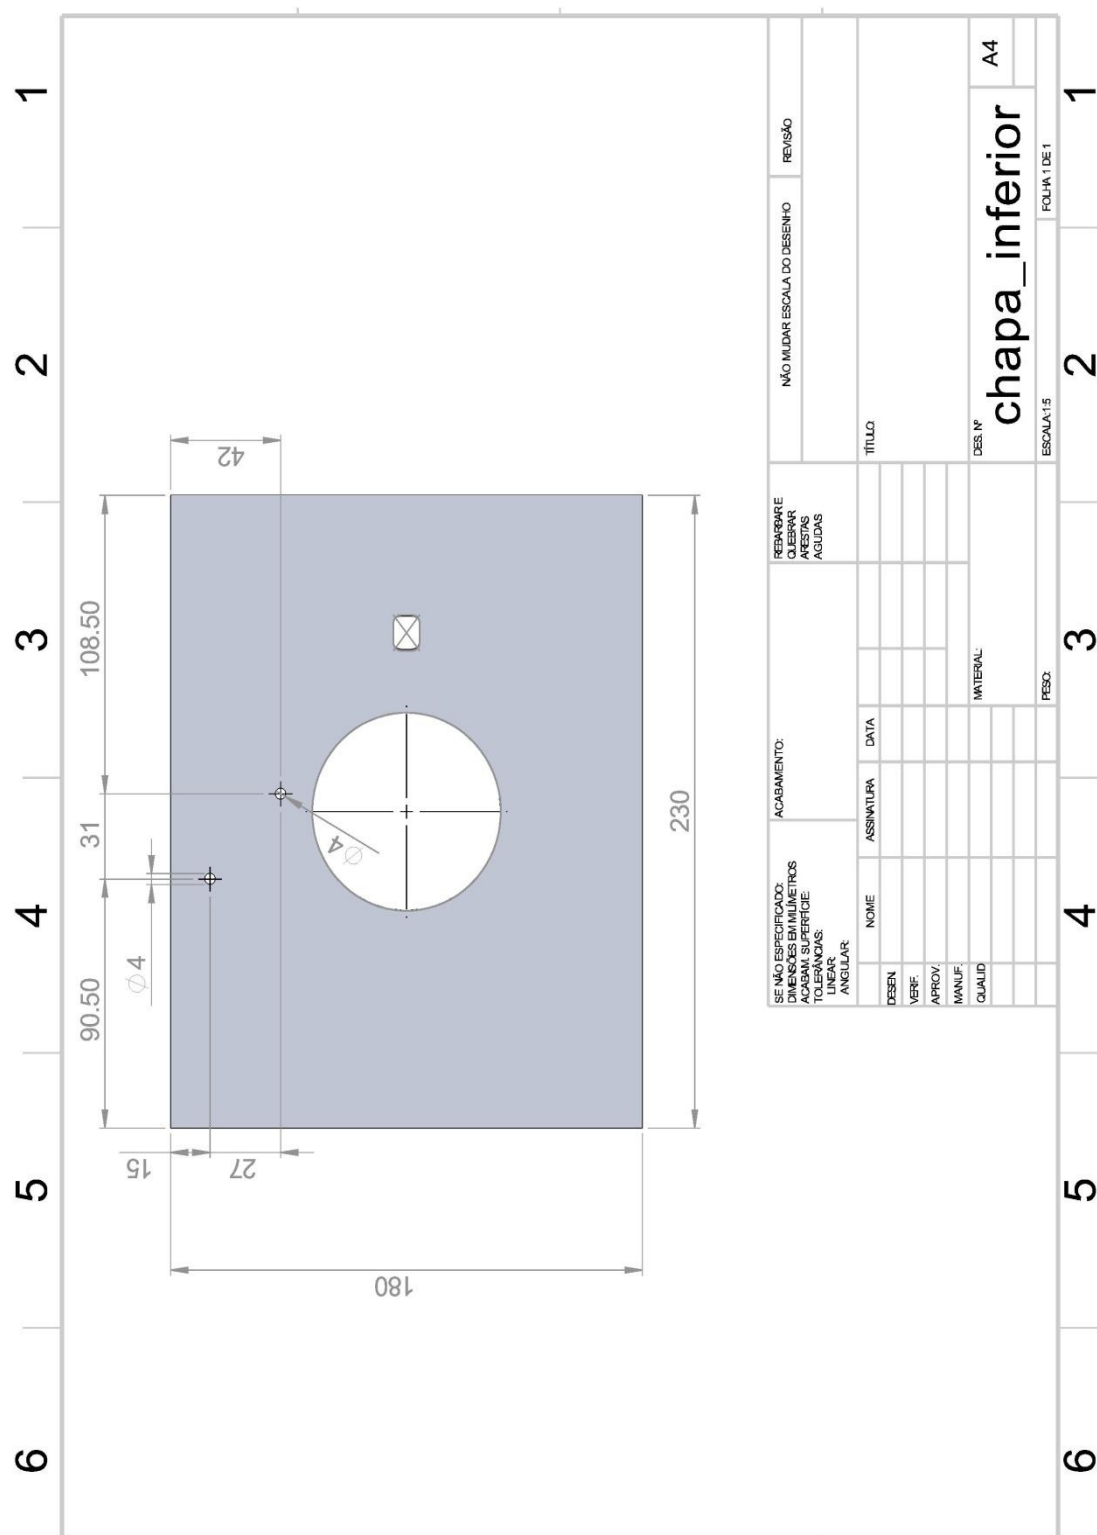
Desenho técnico 2D da chapa inferior para a fixação do fusível DIAZED
